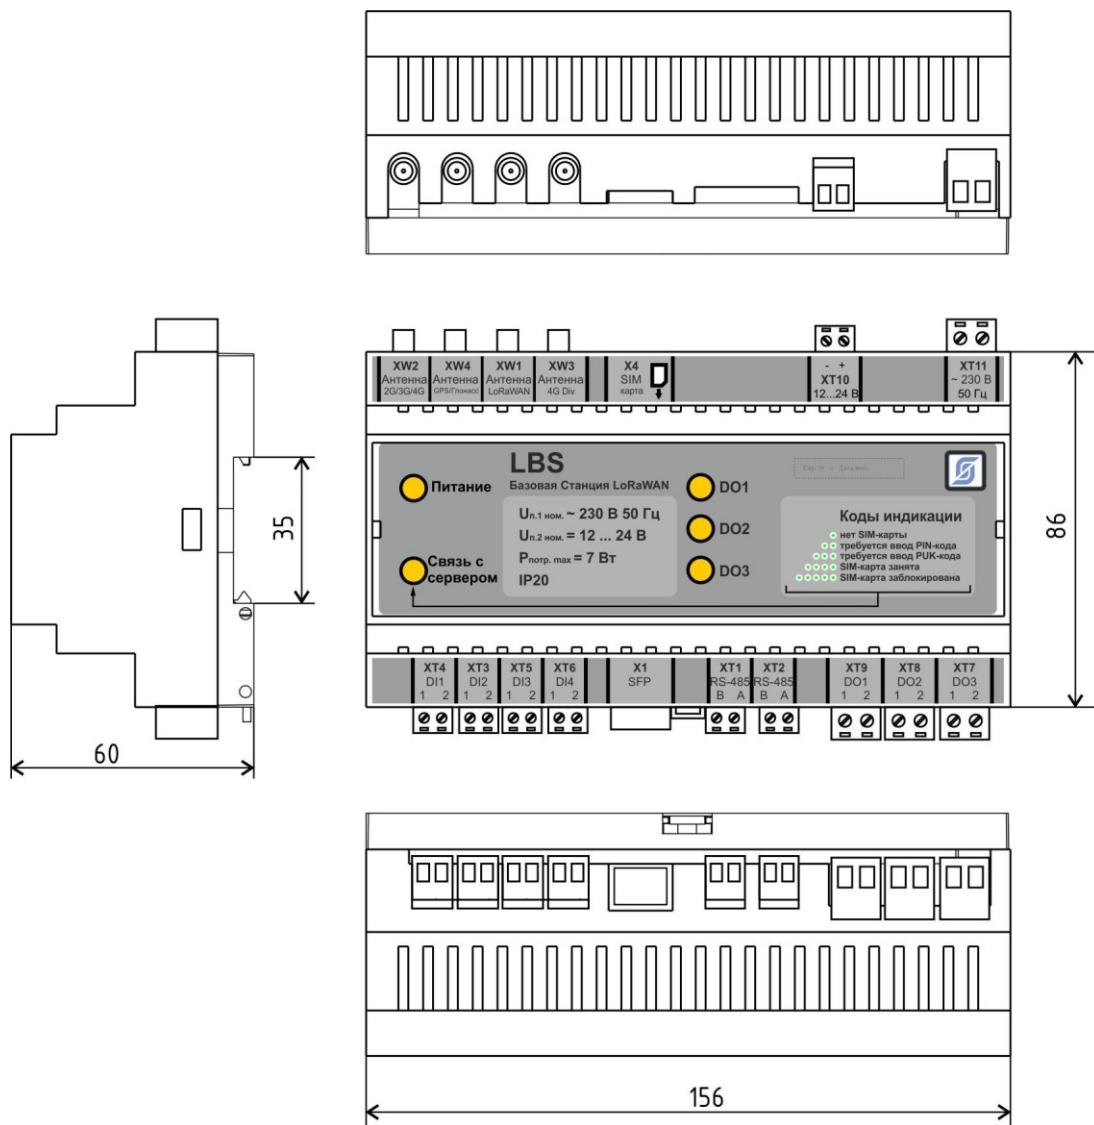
Габаритные и установочные размеры базовой станции "LBS"
